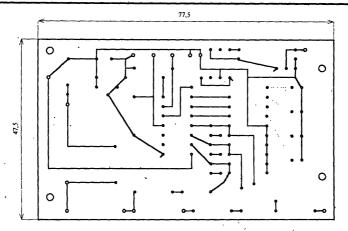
Устройство защиты трехфазных двигателей. Печатная плата
